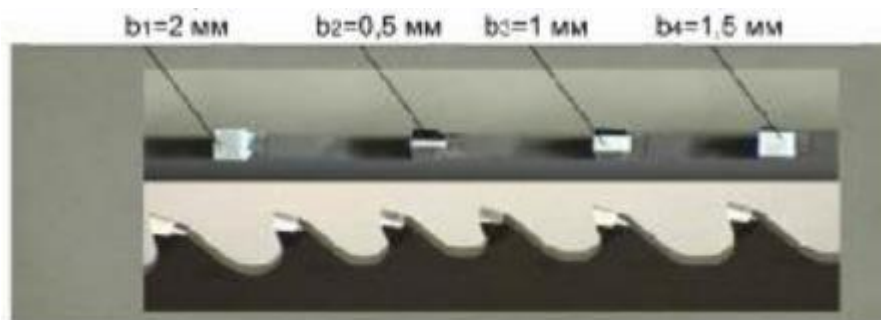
Конструктивні елементи стрічкової пили із зубами з твердого сплаву.
